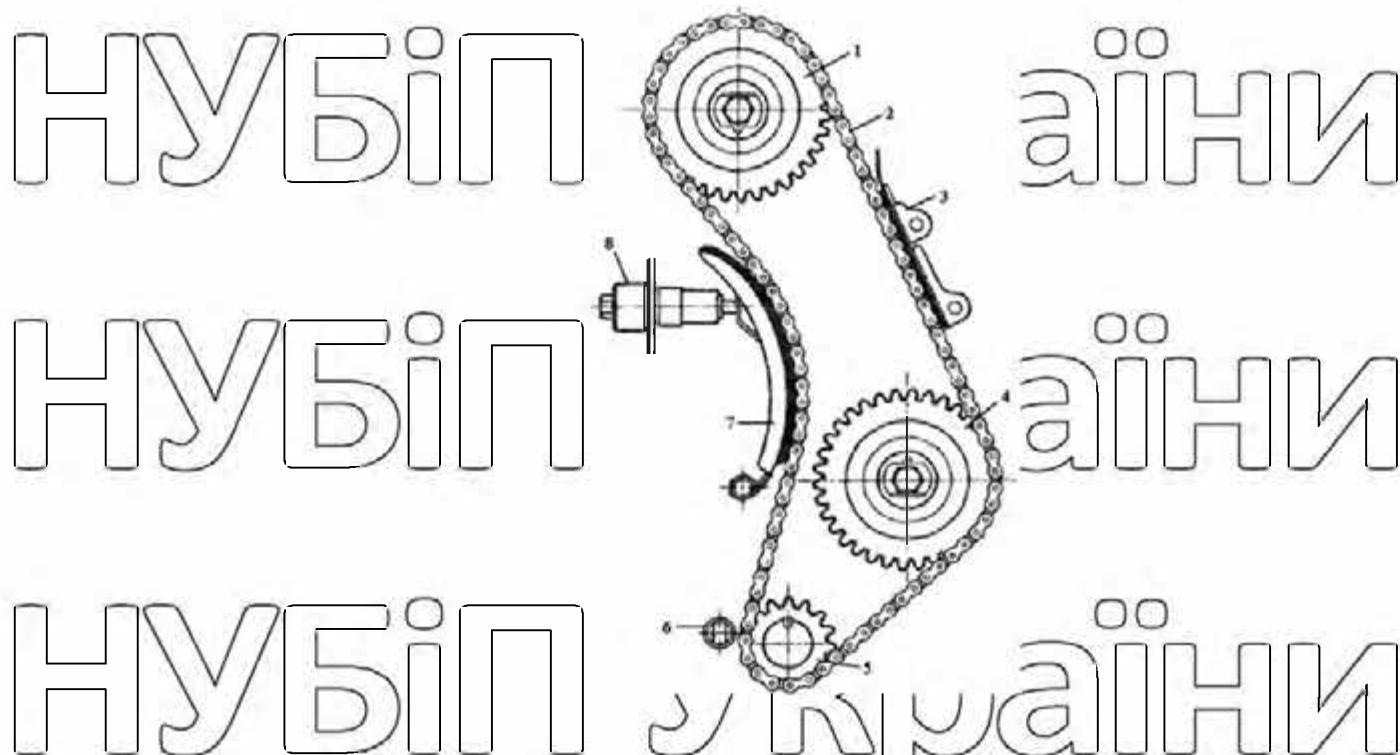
Деталі і схема ланцюгового приводу РВ: 1 - зірочка розподільного валу; 2 - ланцюг; 3 - заспокоювач ланцюга; 4 - зірочка валу допоміжних механізмів; 5 - зірочка колінчастого валу; 6 - обмежувальний палець; 7 - черевик натяжителя; 8 - плунжерний натяжитель ланцюга.
